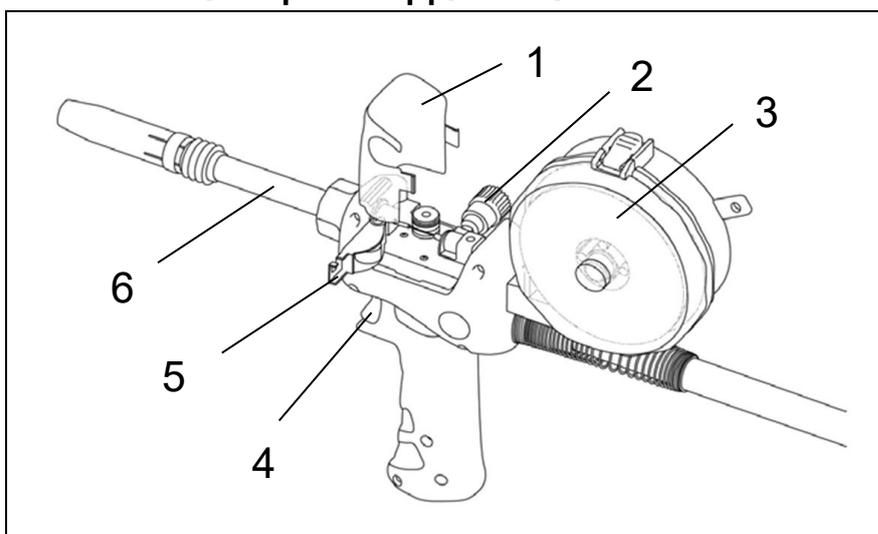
Общий вид сварочной горелки Spool Gun
